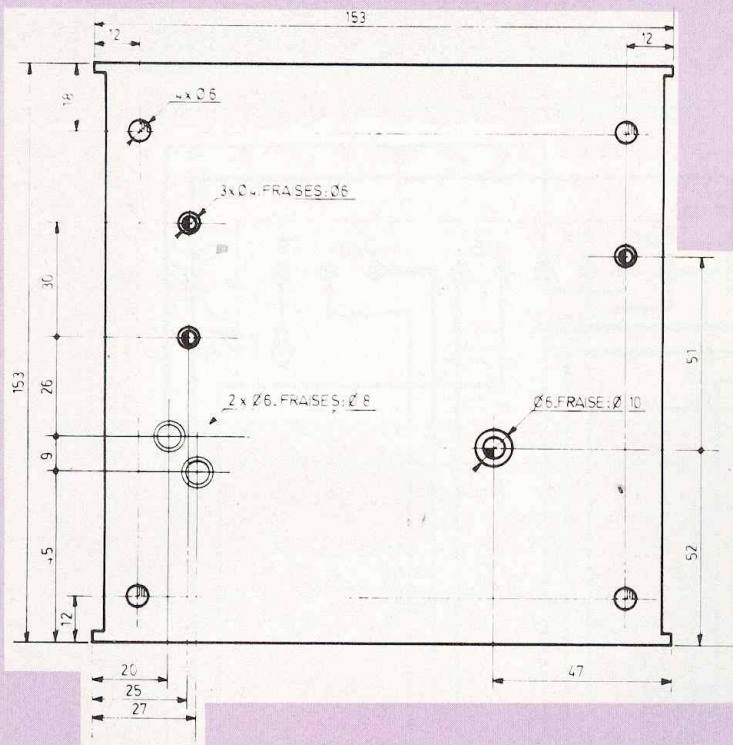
Usinage du dessous du coffret. Ne pas oublier de fraiser les trous.
